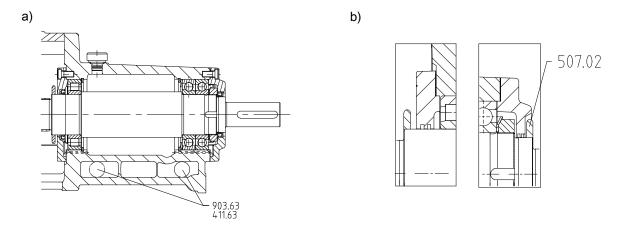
a) Ausführung mit kühlbarem Lagerträger, b) Ausführung mit Labyrinthdichtung
